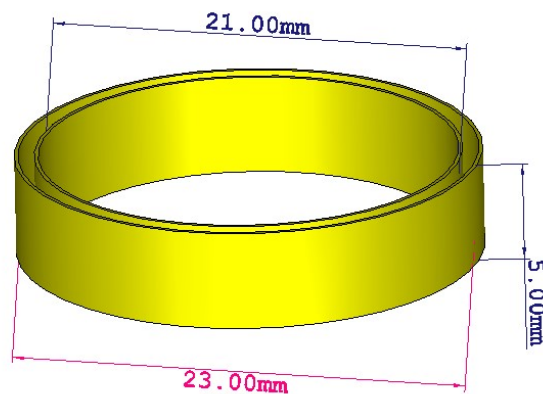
Внешний вид и линейные размеры двойного цилиндрического кольца конечной высоты.
